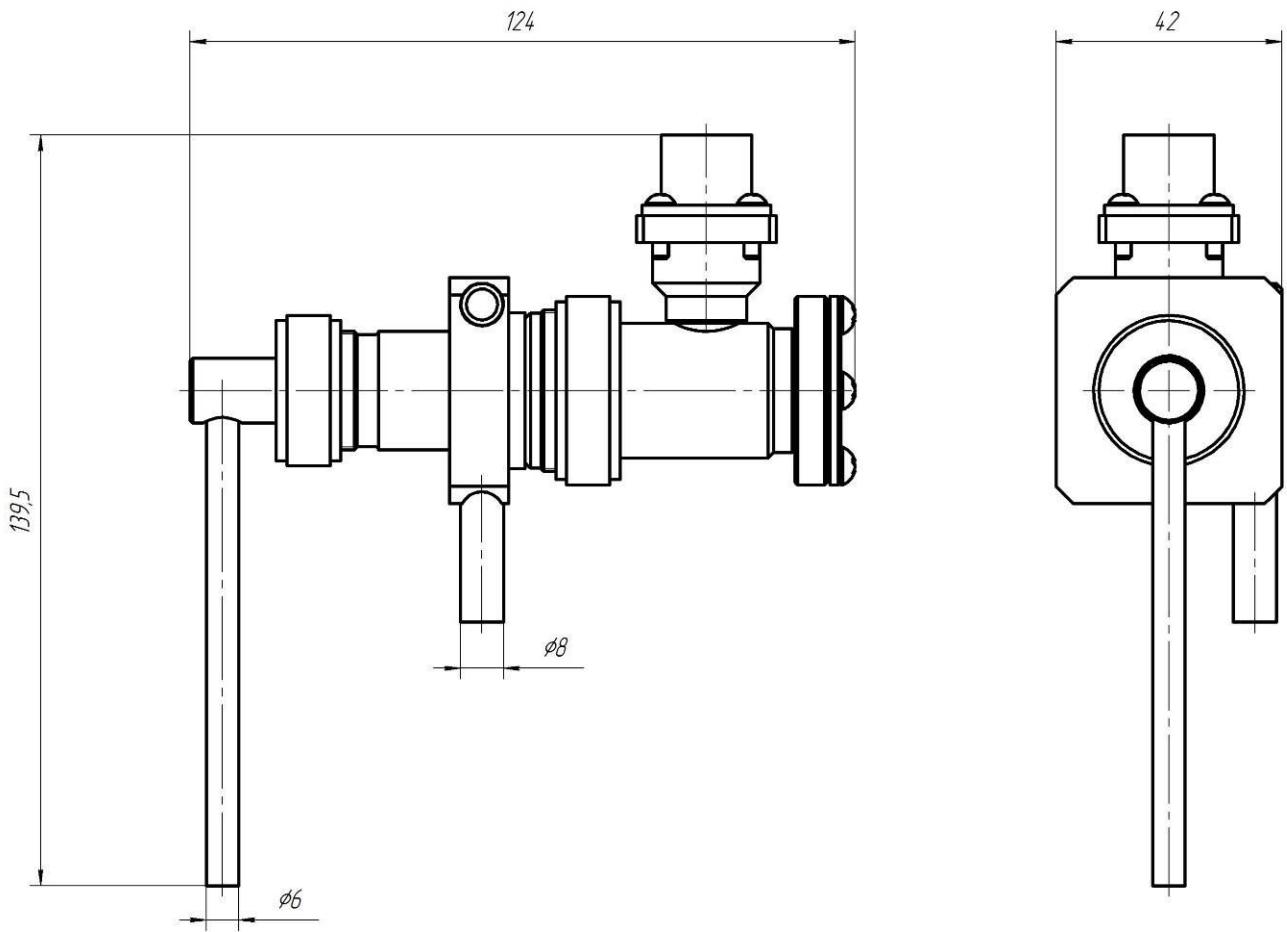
Габаритный чертеж проточного блока датчиков ДК-7.
